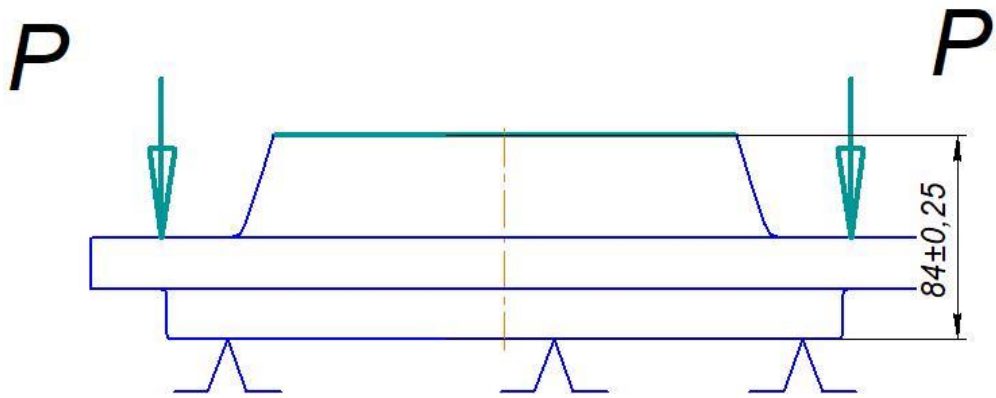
Схема базування і закріплення деталі на операції 005
